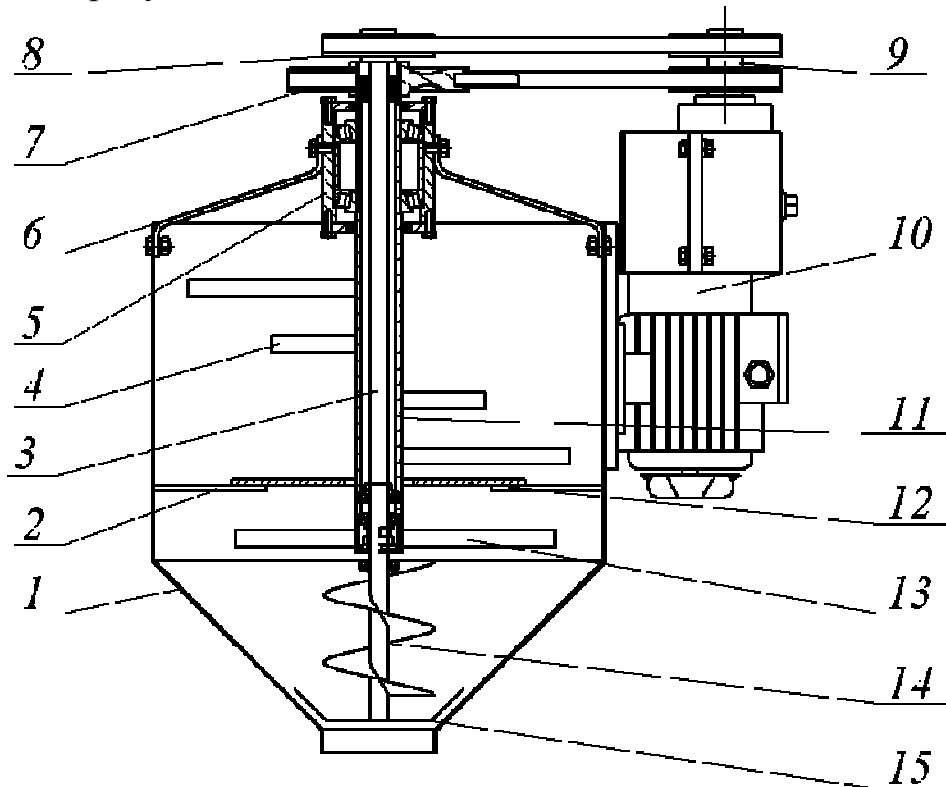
Конструктивно-технологическая схема смесителя-дозатора концентрированных кормов для приготовления предварительной смеси, поступающей на экструзию: 1 – корпус; 2 – луч; 3 – вал; 4 – радиальные лопасти лопастной мешалки; 5 – подшипниковый узел; 6 – распорки; 7 – шкив привода лопастного вала; 8 – шкив привода шнекового вала; 9 – блок шкивов; 10 – мотор-редуктор; 11 – вал привода лопастей; 12 – диск; 13 – спиральные лопасти; 14 – шнек шнековой мешалки; 15 – лопатки якорного ворошителя
